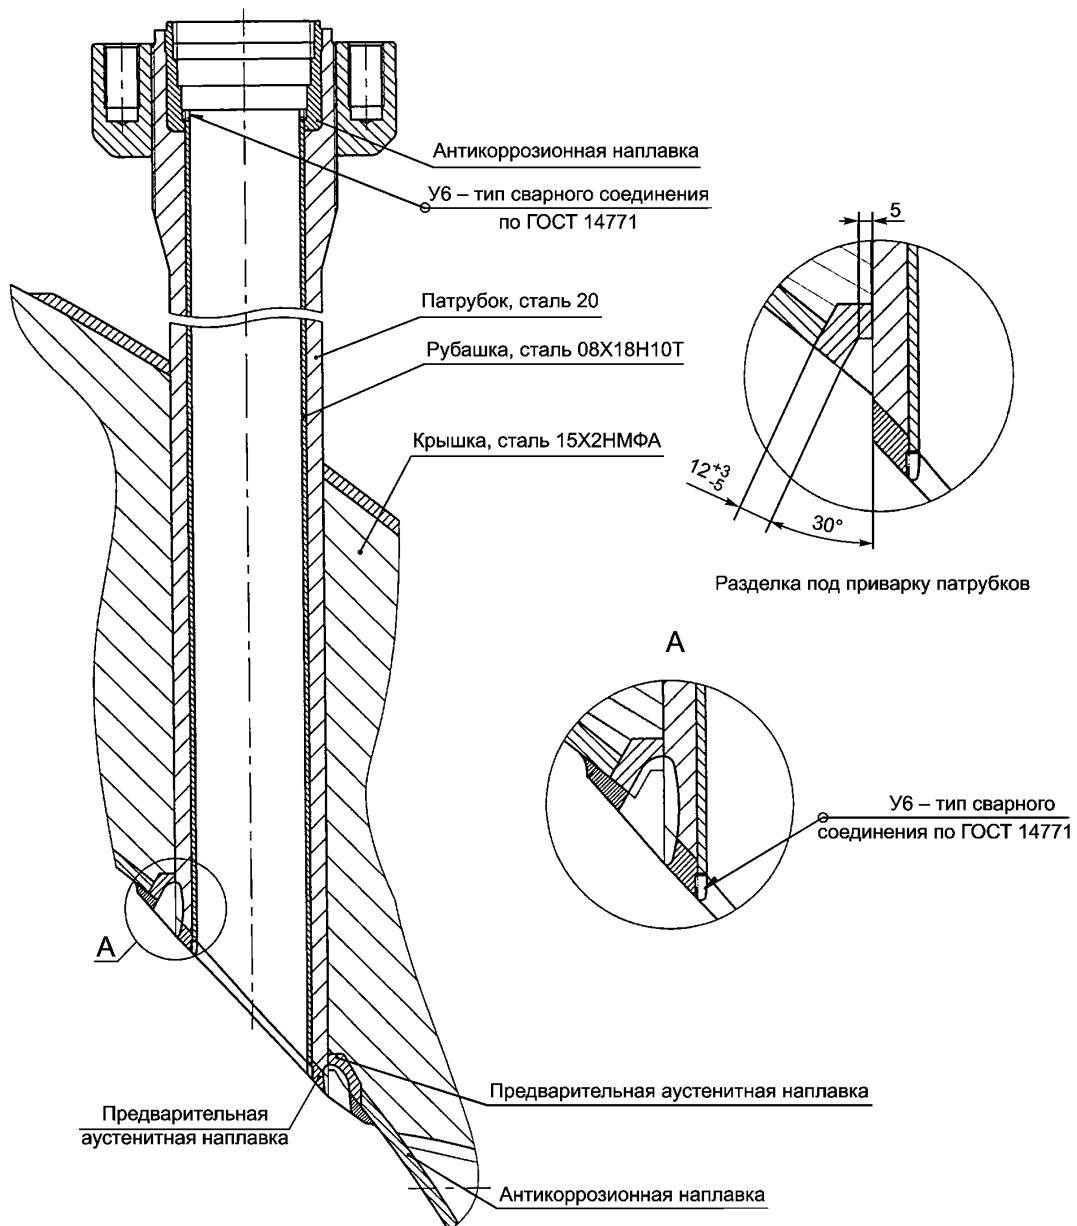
Крышка корпуса реактора в районе приварки патрубка
